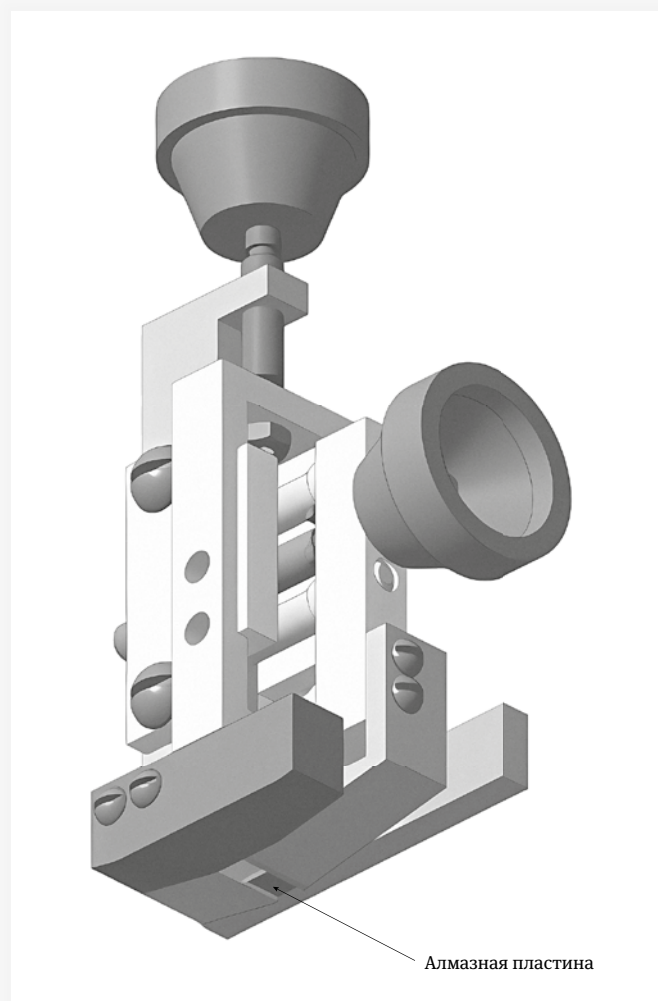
Внешний вид зажима приспособления для механического крепления пластин алмаза при полировке
